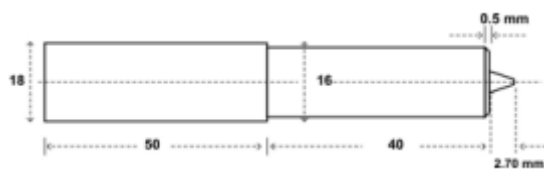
Exemple de dimensions d'un outil pour le soudage des AA6351 [14]
